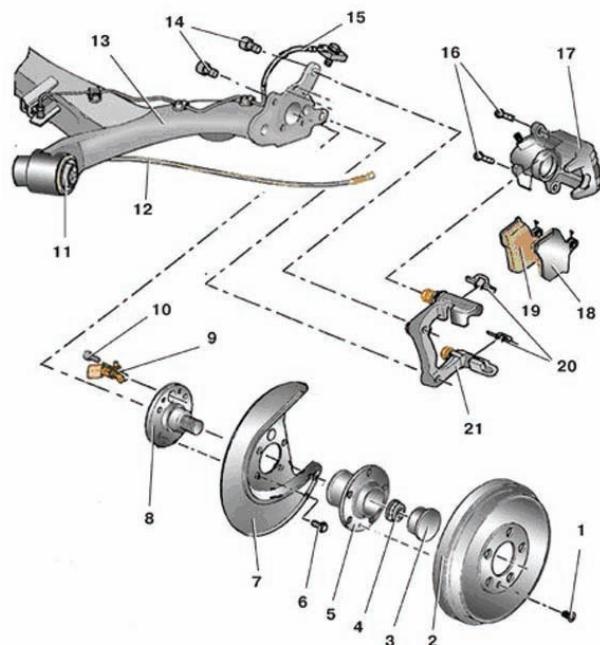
Детали тормозного дискового механизма заднего колеса. 1 – винт; 2 – тормозной диск; 3 – защитный колпачок; 4 – гайка ступицы; 5 – ступица; 6 – болт крепления тормозного щита; 7 – тормозной щит; 8 – цапфа оси; 9 – датчик частоты вращения колеса; 10 – болт крепления датчика; 11 – резинометаллическая опора; 12 – трос привода стояночного тормоза; 13 – балка задней подвески; 14 – болты крепления направляющей колодок; 15 – тормозной шланг; 16 – болты крепления суппорта; 17 – суппорт; 18 – наружная тормозная колодка; 19 – внутренняя тормозная колодка; 20 – пружинный фиксатор; 21 – направляющая колодок
